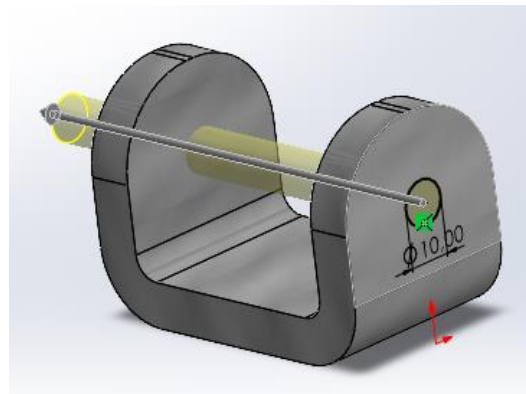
Corte horquillas de la junta cardán en SolidWorks.
